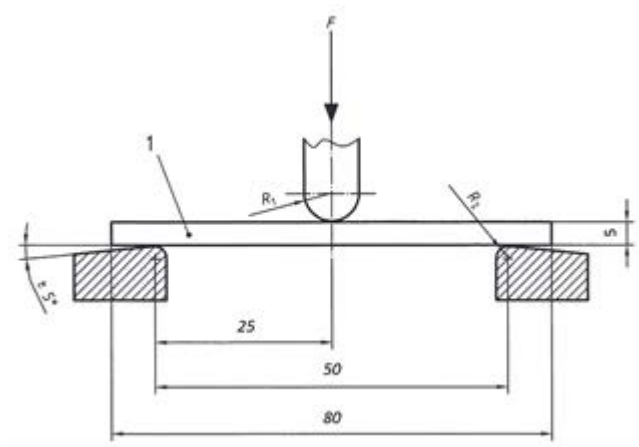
Dimensiones de la probeta y disposición del ensayo de flexión en tres puntos (mm)
